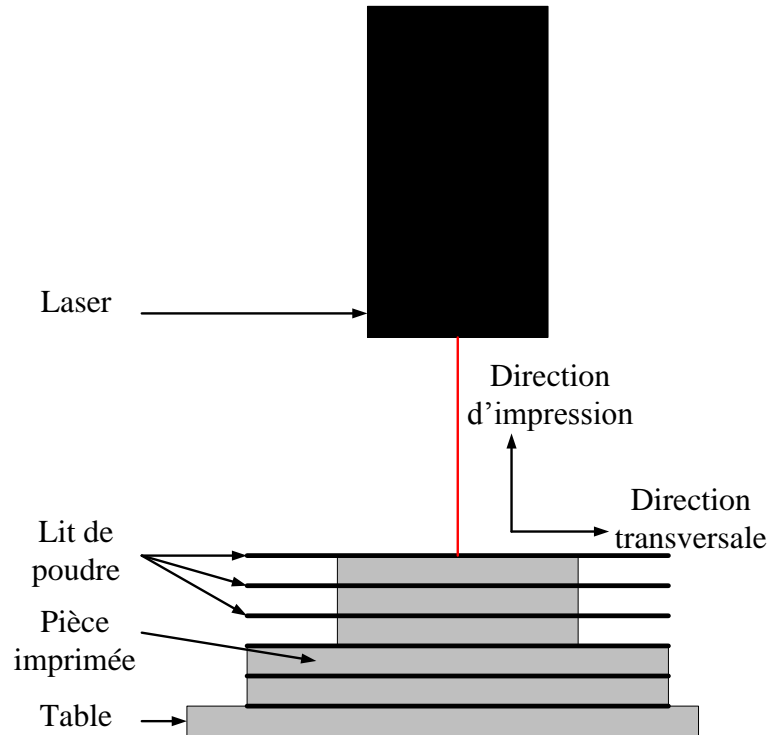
Schéma du procédé de fabrication additive des pièces d'Inconel 718 FA
